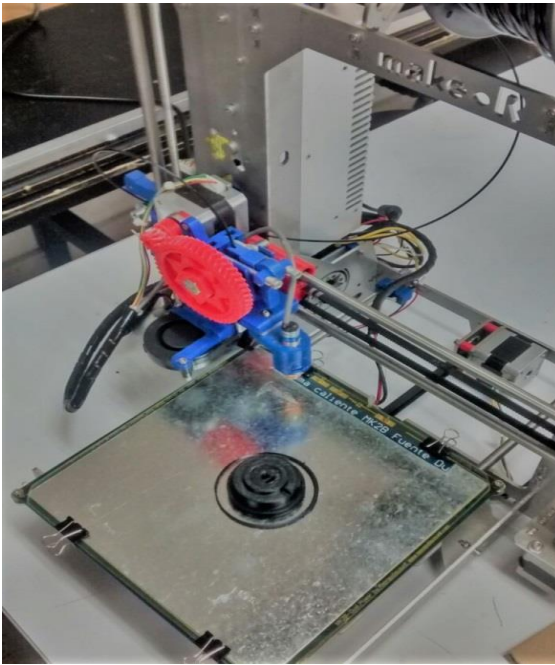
Impresión del Housing o carcasa con la impresora 3D.
